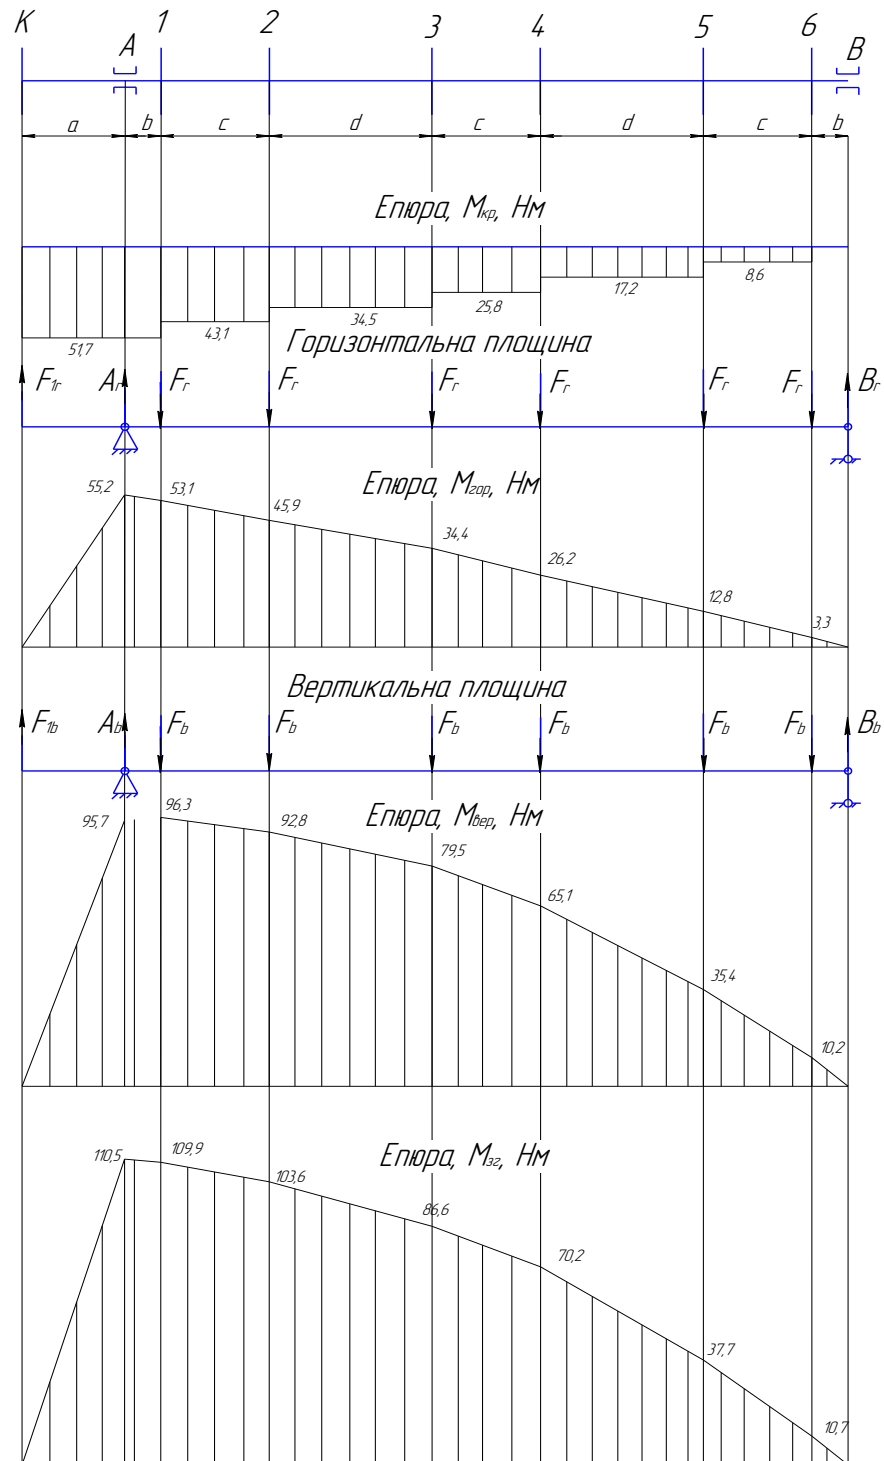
Розрахункова схема вала з епюрами моментів
